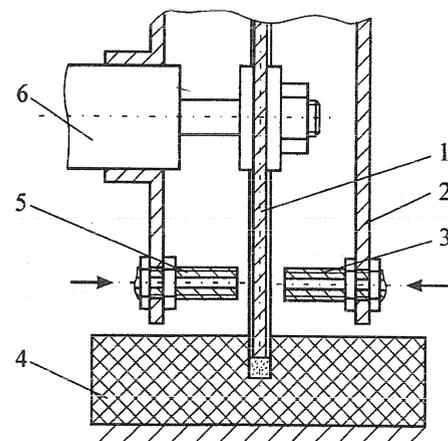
Схема экспериментальной установки на базе станка "GS-400": 1 – отрезной круг; 2 – кожух; 3, 5 – насадки; 4 – заготовка; 6 – шпиндель станка
